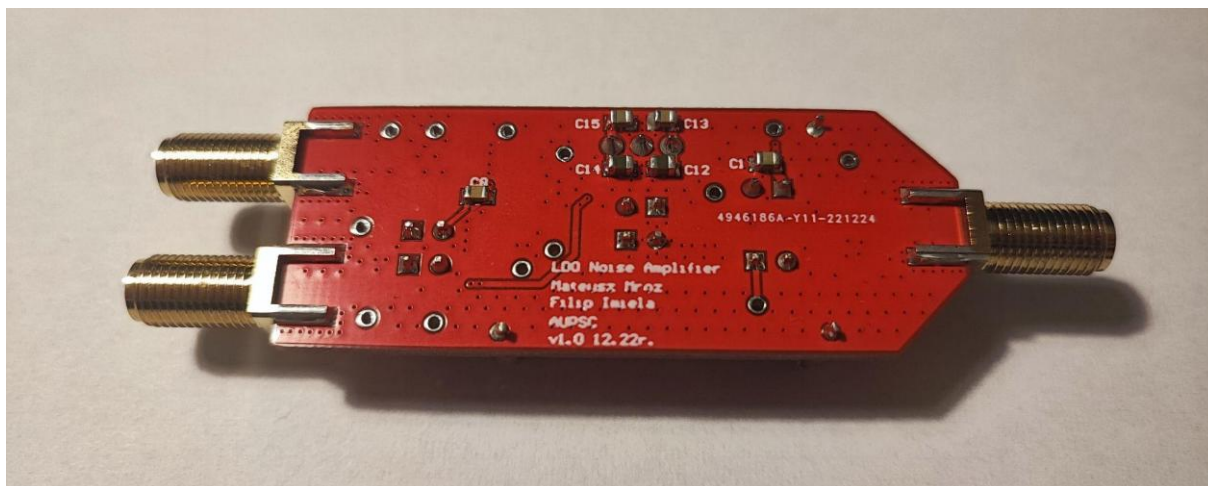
Widok 3D zaprojektowanego układu z dołu
